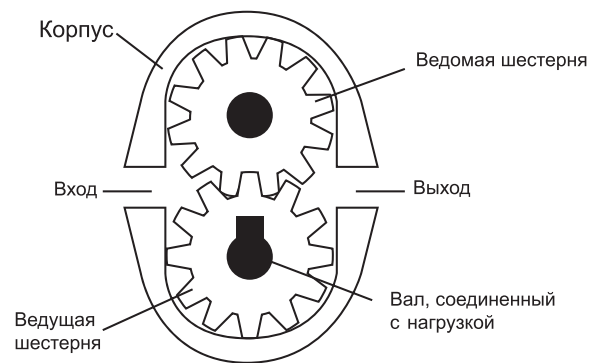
Компоненты типичного шестерённого гидромотора
